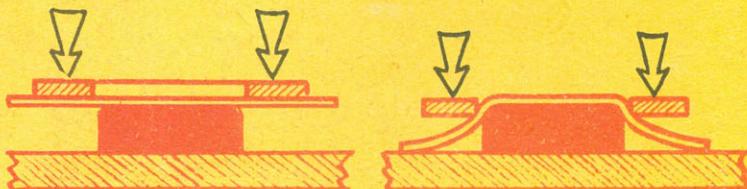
Заготовка корпуса: 1 — болванка-шаблон, 2 — прижимная рамка.
